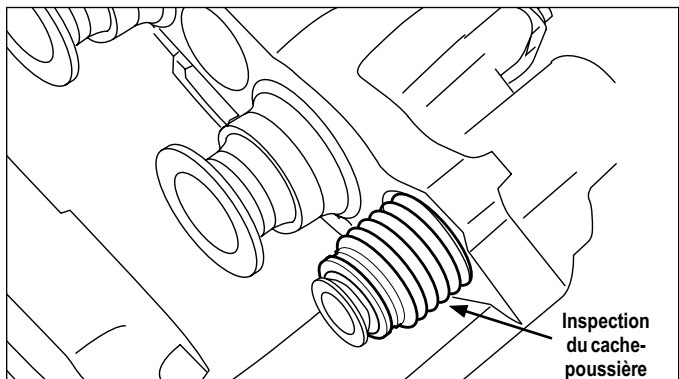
INSPECTION DU CACHE-POUSSIÈRE DE LA TIGE DE GUIDAGE (CETTE ILLUSTRATION NE MONTRE PAS LE PLATEAU PORTEUR)
